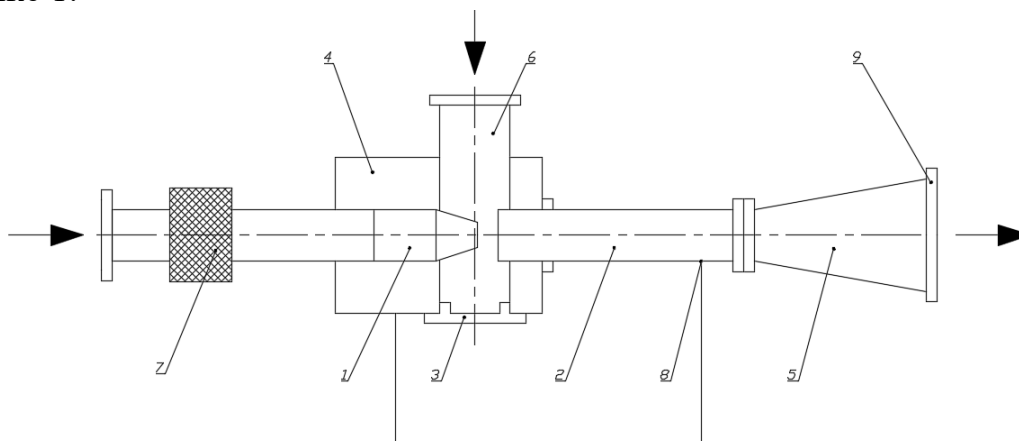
1 – сопло; 2 – камера смешения; 3 – крышка корпусная; 4 – корпус; 5 – диффузор; 6 – отвод боковой; 7 – фильтр; 8 – рама; 9 – фланцы.
